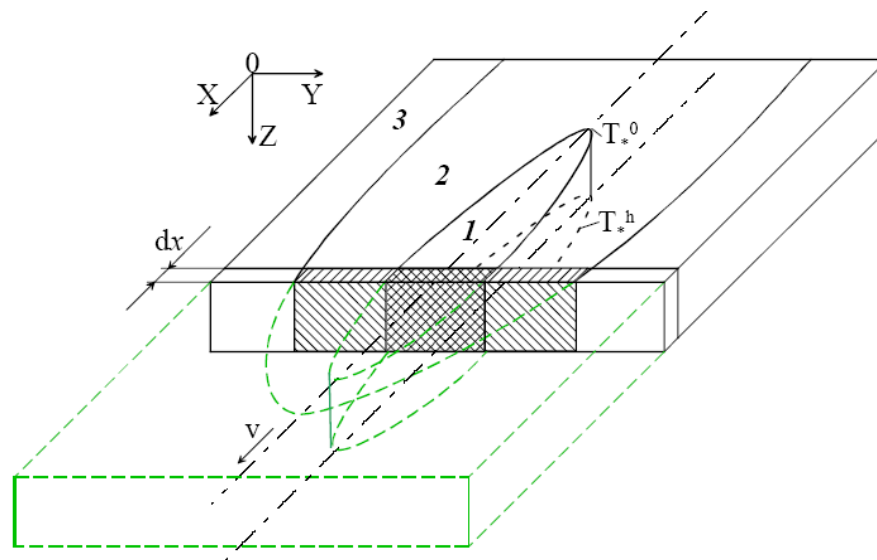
Zonas del metal soldado ¹⁰
